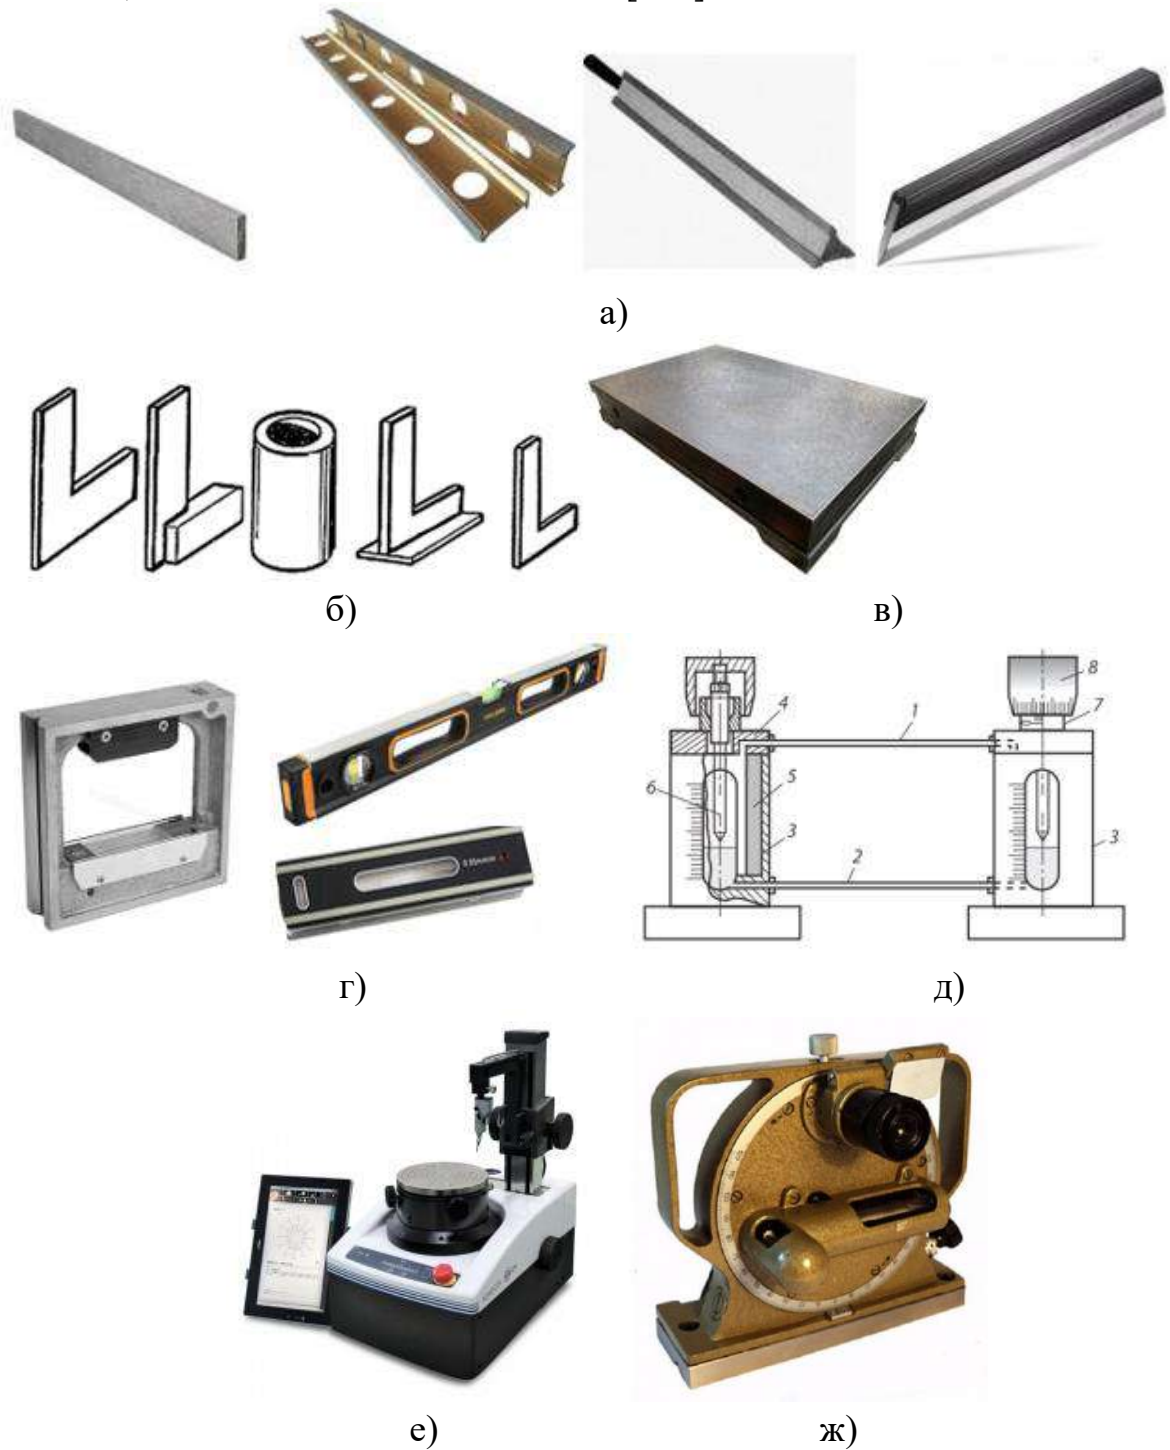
Інструменти для контролю форми і розташування поверхонь
